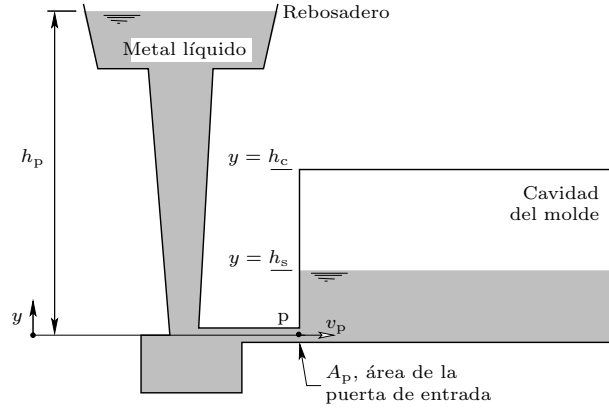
Llenado por la parte inferior de la cavidad del molde.
